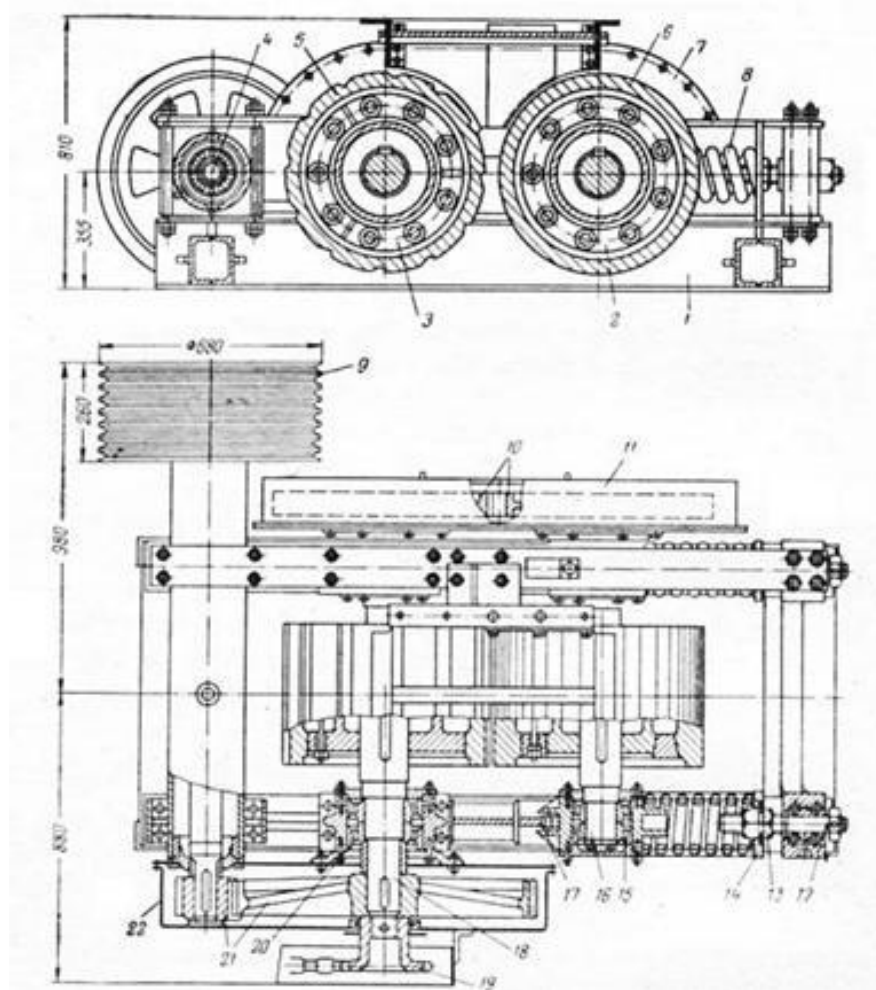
Схема двовалкової дробарки з гладкими валками: 1 – рама; 2, 3 – валки; 4 – вал контрпривода; 5, 6 – змінний бандаж валків; 7 – кришка дробарки з лійкою для завантаження; 8 – пружина; 9 – шків контрпривода; 10 – зубчата пара; 11 – захисний кожух; 12 – упорна шпилька; 13 – гайки для регулювання; 14 – шайба; 15 – підшипник; 16 – вісь валка; 17 – змінна прокладка; 18 – вісь нерухомого валка; 20 – нерухомий підшипник; 21 – зубчата пара; 22 – кожух
